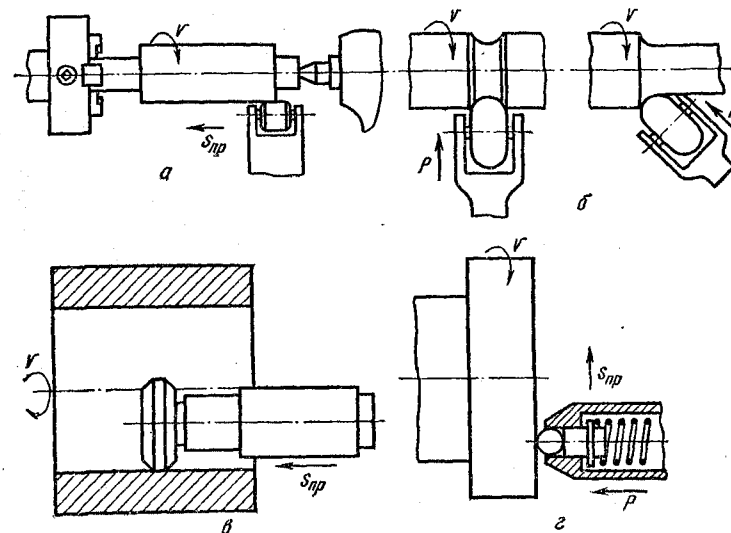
Схемы обкатывания и раскатывания поверхностей заготовок
